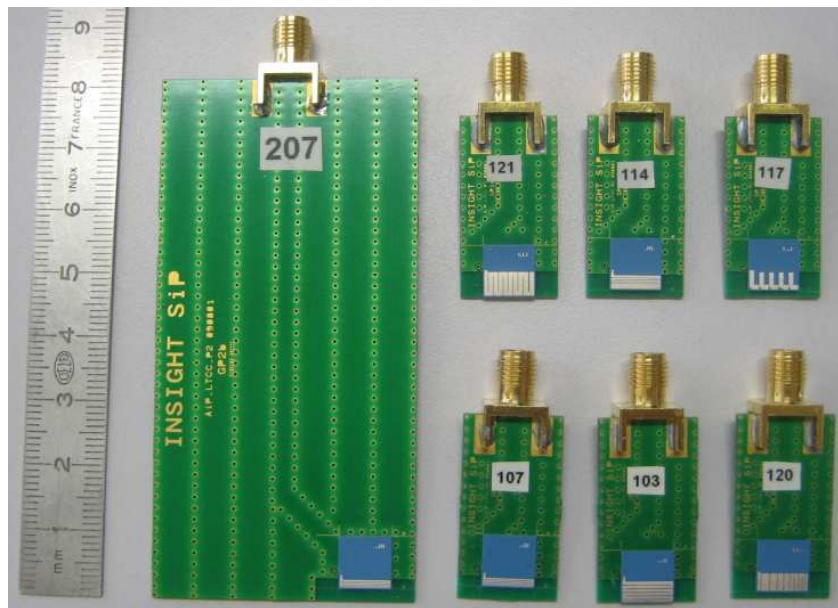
Photographie de plusieurs prototypes soudés sur deux types de PCB
